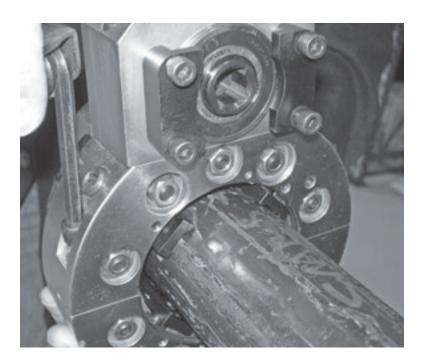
Serrez les vis de blocage du châssis pour fixer la machine SDSF autour du tuyau en ligne.
